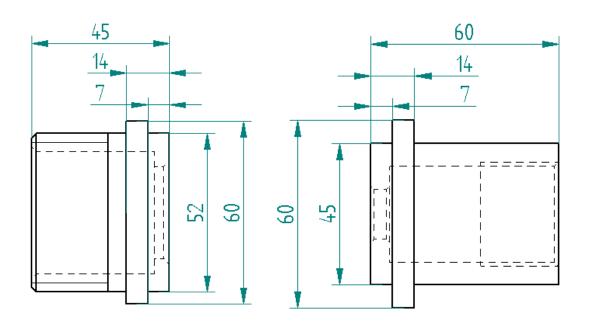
Dimensiones de las bridas de soldadura
